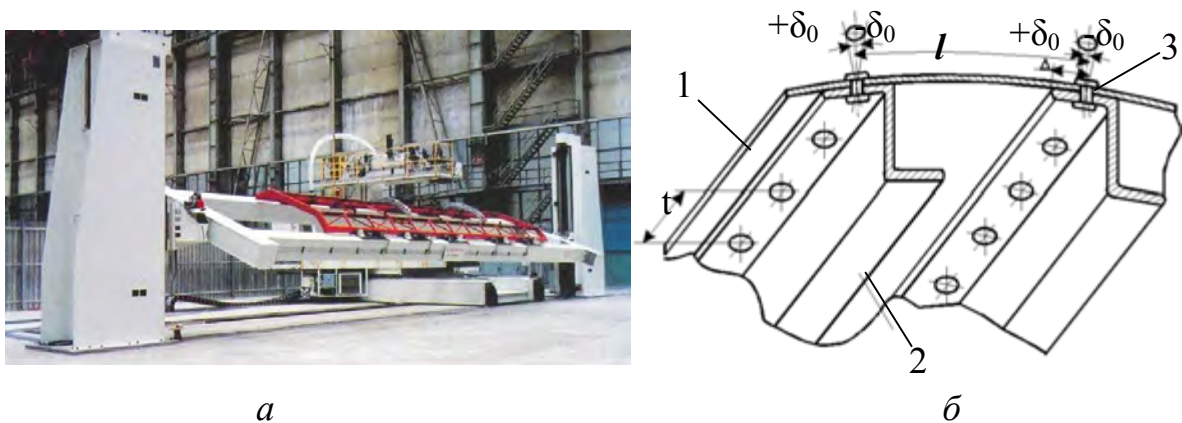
Установка Gemcor 5013 TTX-128/G86: *а* - общий вид установки; *б* - зона клепки собираемого изделия: 1- обшивка; 2 – стрингер; 3 – заклепка
